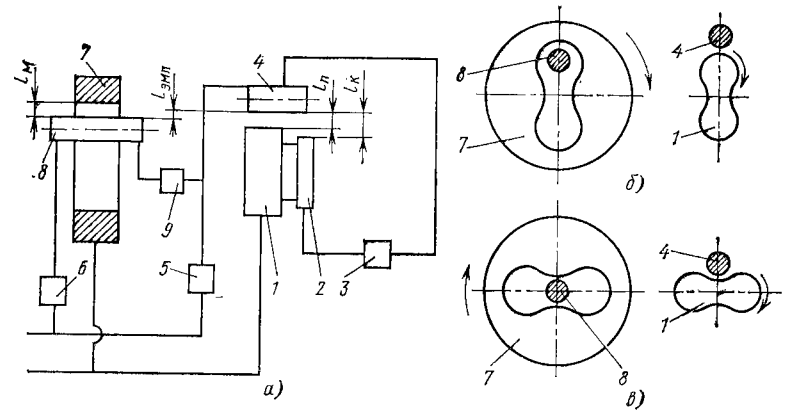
Принципиальная схема одновременной обработки двух сопрягаемых деталей различными инструментами (а) и их расположение относительно обрабатываемых деталей (б, в)
